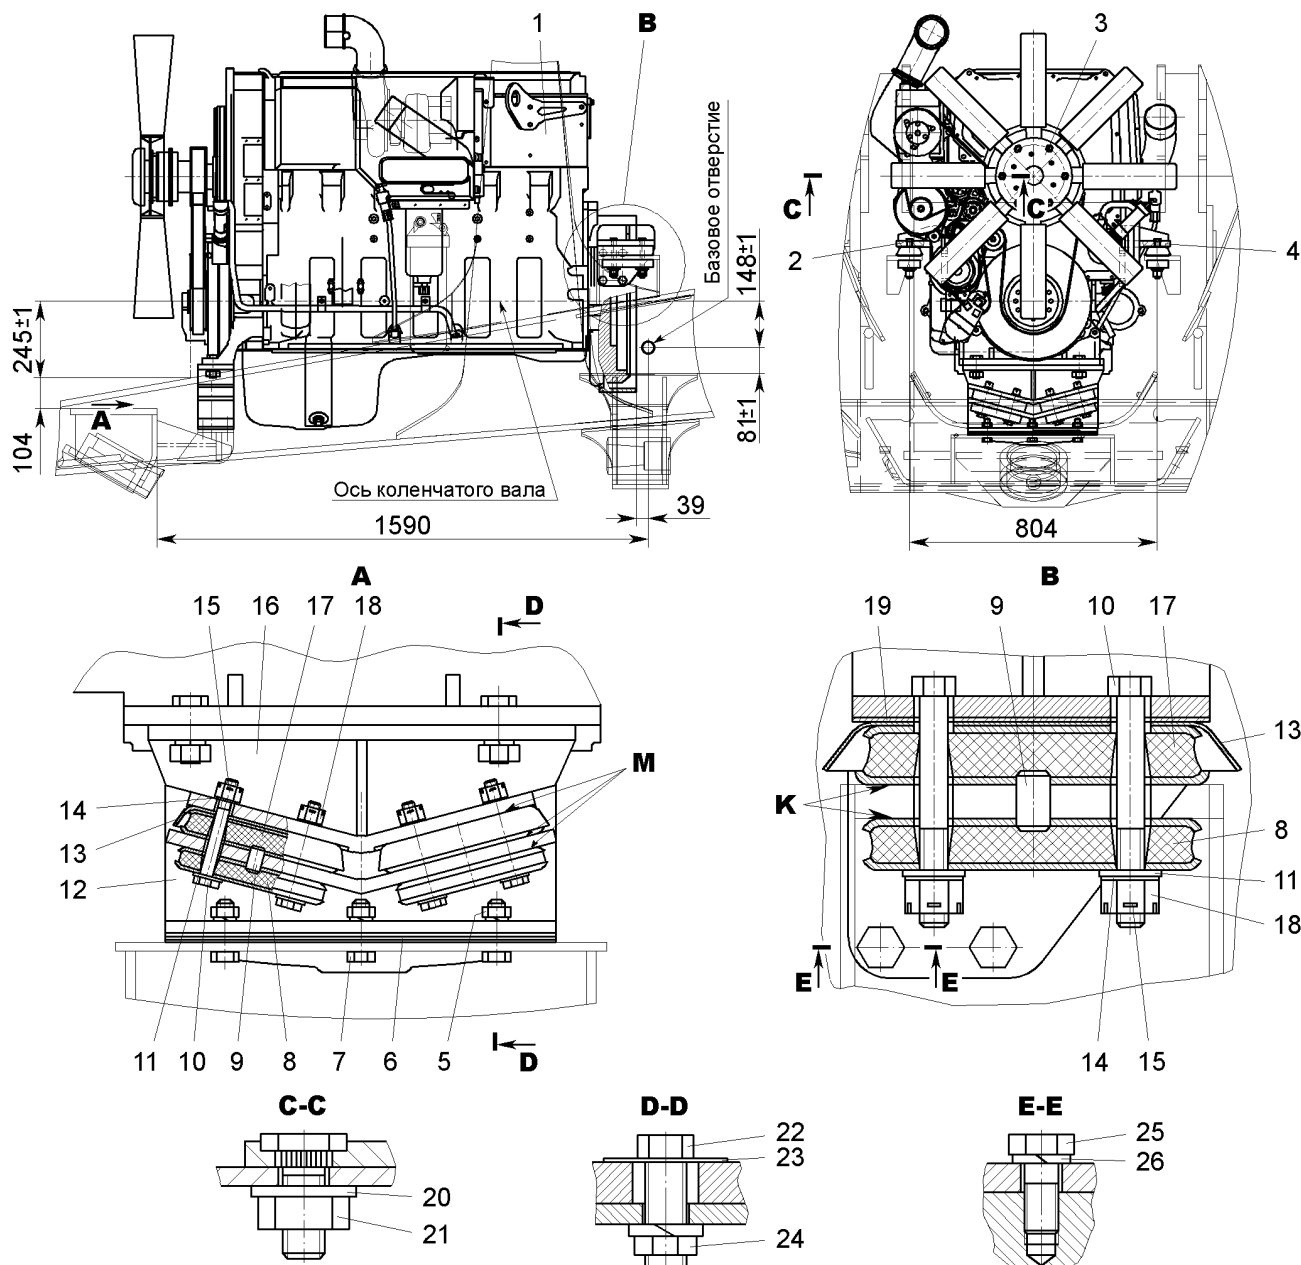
Установка двигателя самосвала БелАЗ-75450:
